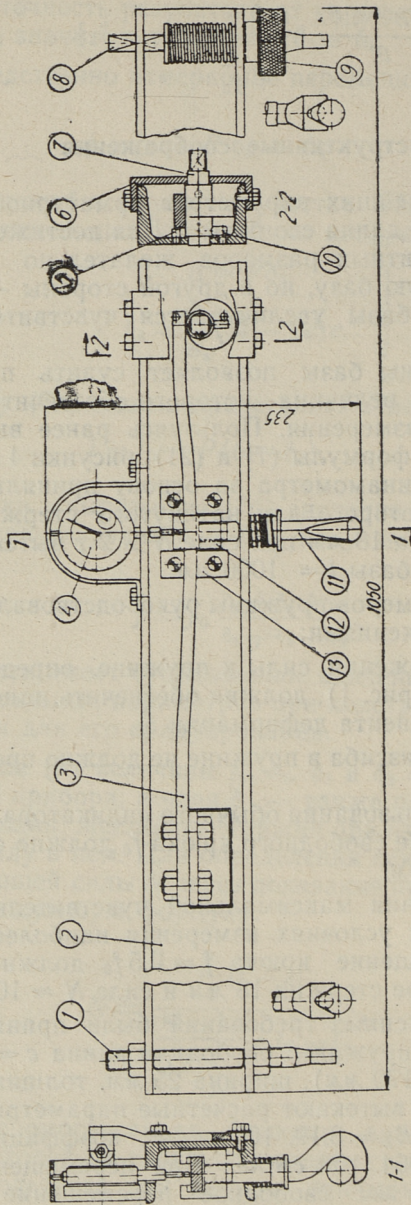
Общий вид арматурного динамометра АД-59. 1 — опорный болт, 2 — корпус, 3 — пружина, 4 — индикатор, 5 — упор, 6 — скоба, 7 — эксцентрик, 8 — подвижный опорный болт, 9 — регулировочная гайка, 10 — ограничитель, 11 — крюк, 12 — ползун, 13 — направляющая планка.
